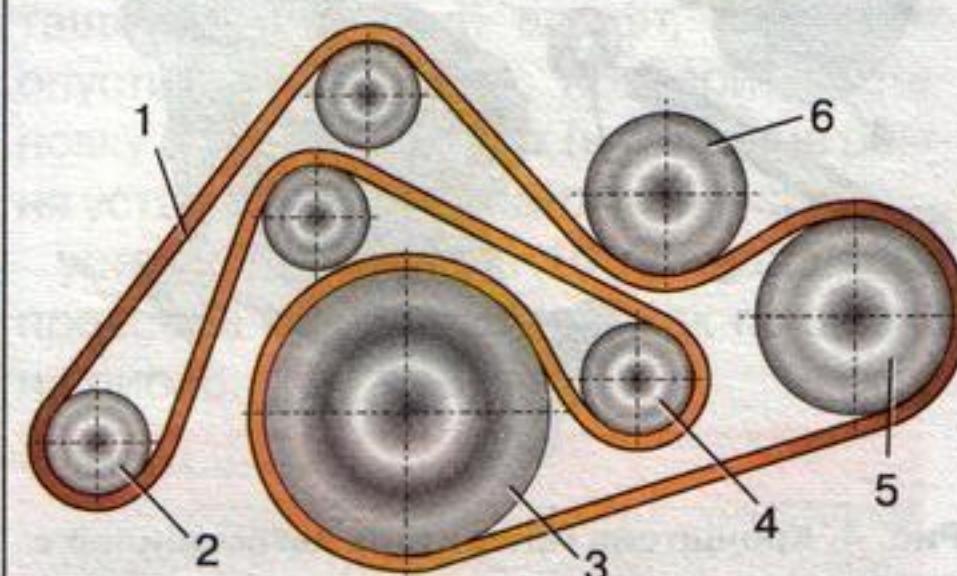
Схема установки ремня привода агрегатов дизельного двигателя рабочим объемом 2,5 л: 1 – ремень привода агрегатов; 2 – шкив генератора; 3 – шкив коленчатого вала; 4 – натяжной ролик; 5 – шкив насоса гидроусилителя рулевого управления; 6 – шкив вентилятора охлаждения двигателя
